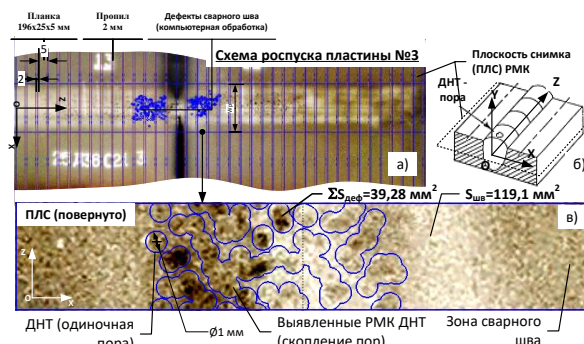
Исследование структуры внутренних ДНТ сварного шва при помощи РМК для разработки схемы роспуска пластины №3 на планки (197x25x5 мм)
